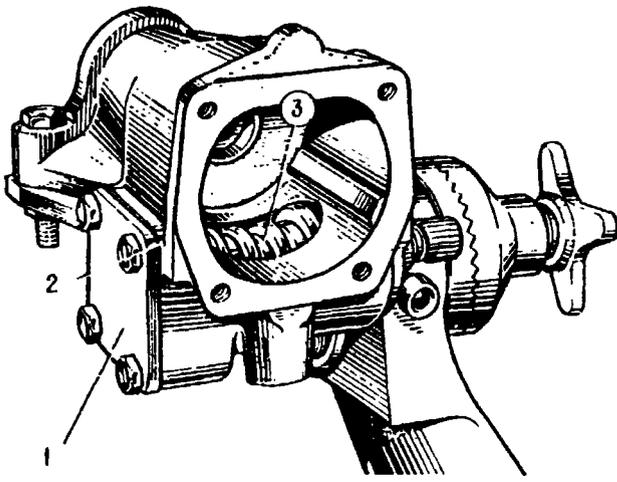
Установка червяка рулевого механизма: 1 - крышка подшипника; 2 - регулировочная прокладка; 3 - червяк
